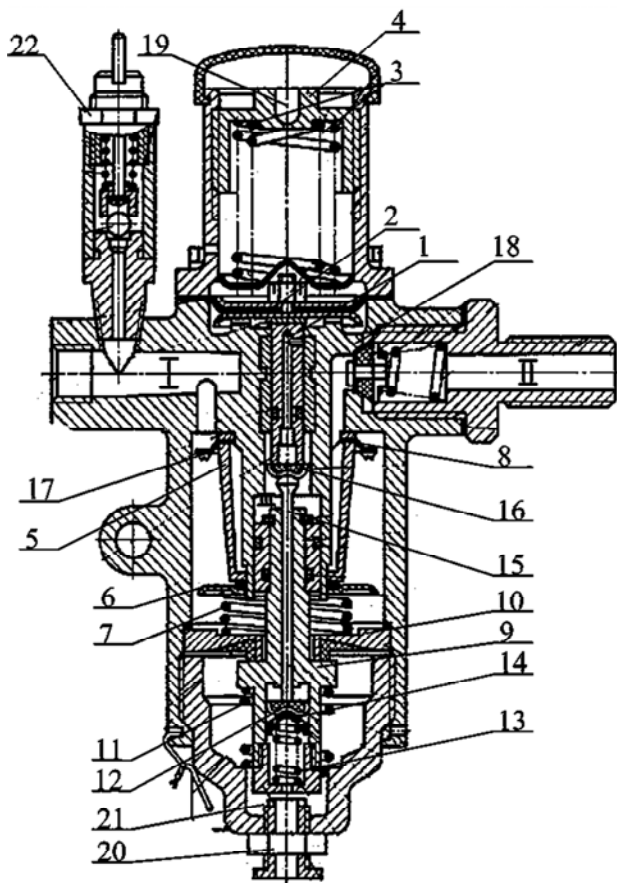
Регулятор давления со схемой установки индикаторов
